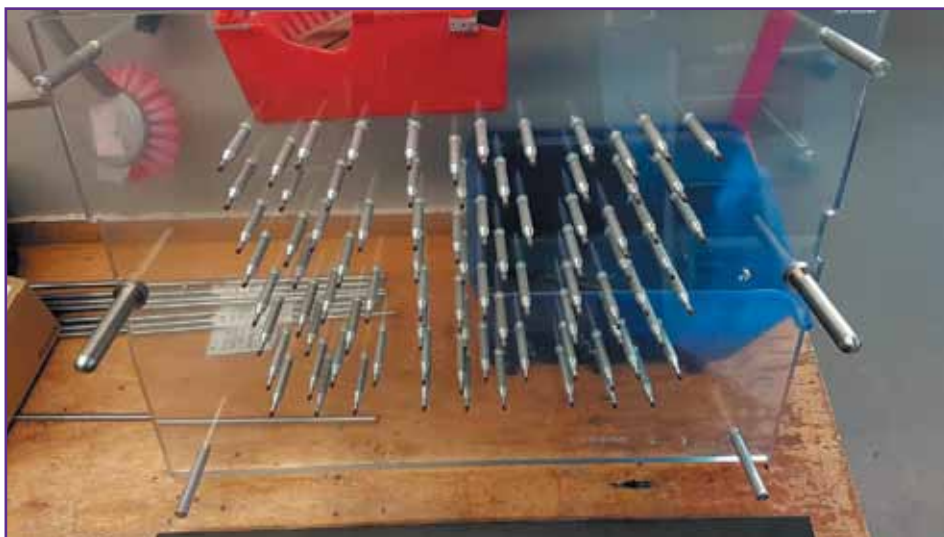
Пластина со стержнями-фиксаторами прижимного механизма
